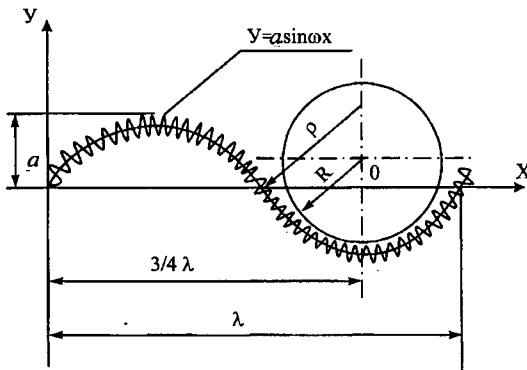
Схема розрахунку геометрії інструмента для тонкого пластичного деформування поверхні.
